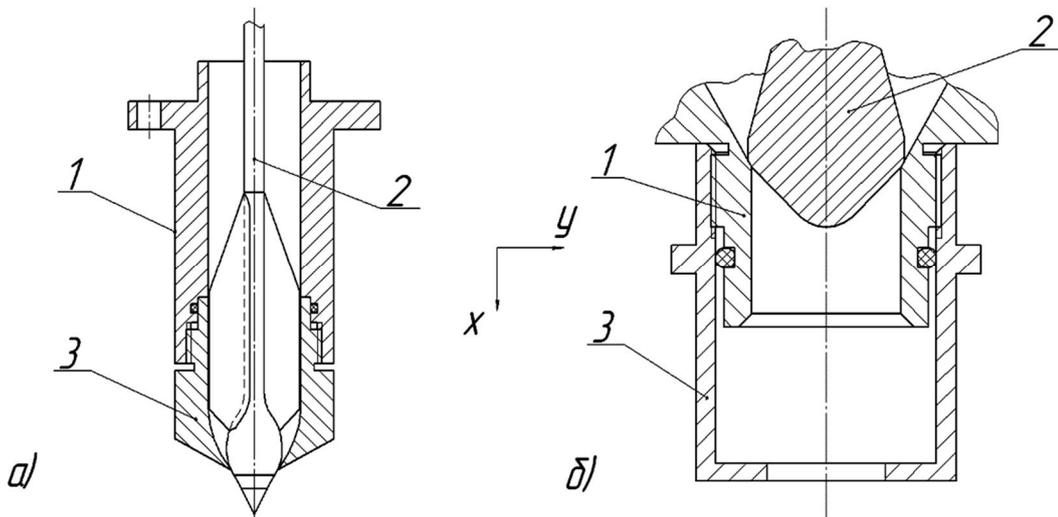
Приклад робочого органа у вагових дозаторах: а) конічна; б) циліндрична насадка: 1 – корпус; 2 – клапан; 3 – насадка
